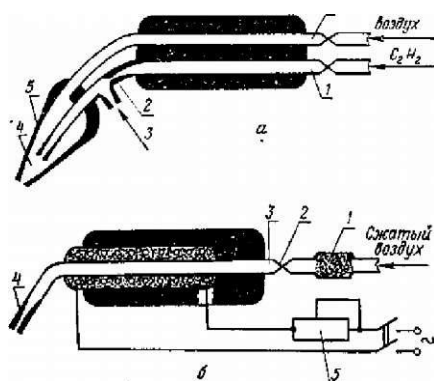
Схема горелок для сварки термопластов горячими газами:
